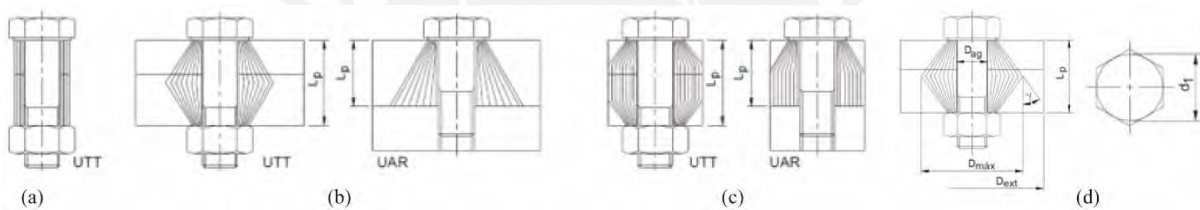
27 Zonas de compresión según las dimensiones de la placa y dimensiones
